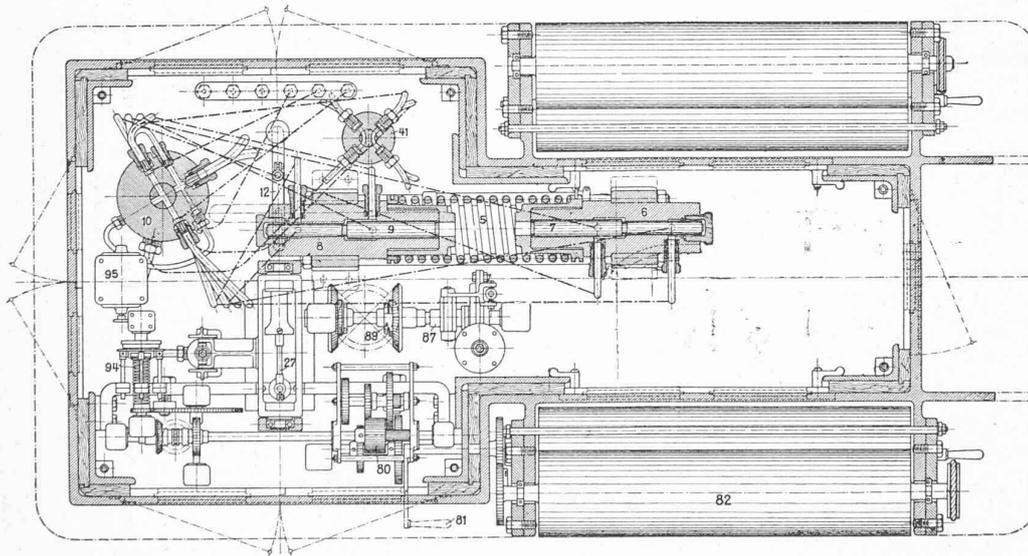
Coupe horizontale au-dessous de la plaque de la table. — Echelle 1 : 12,5.
